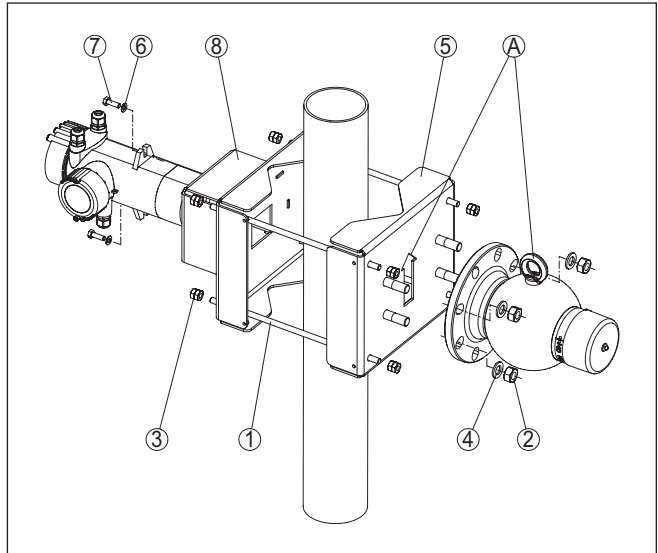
Dispositivo de sujeción con sensor montado horizontalmente (con VEGASOURCE 31, 35)
